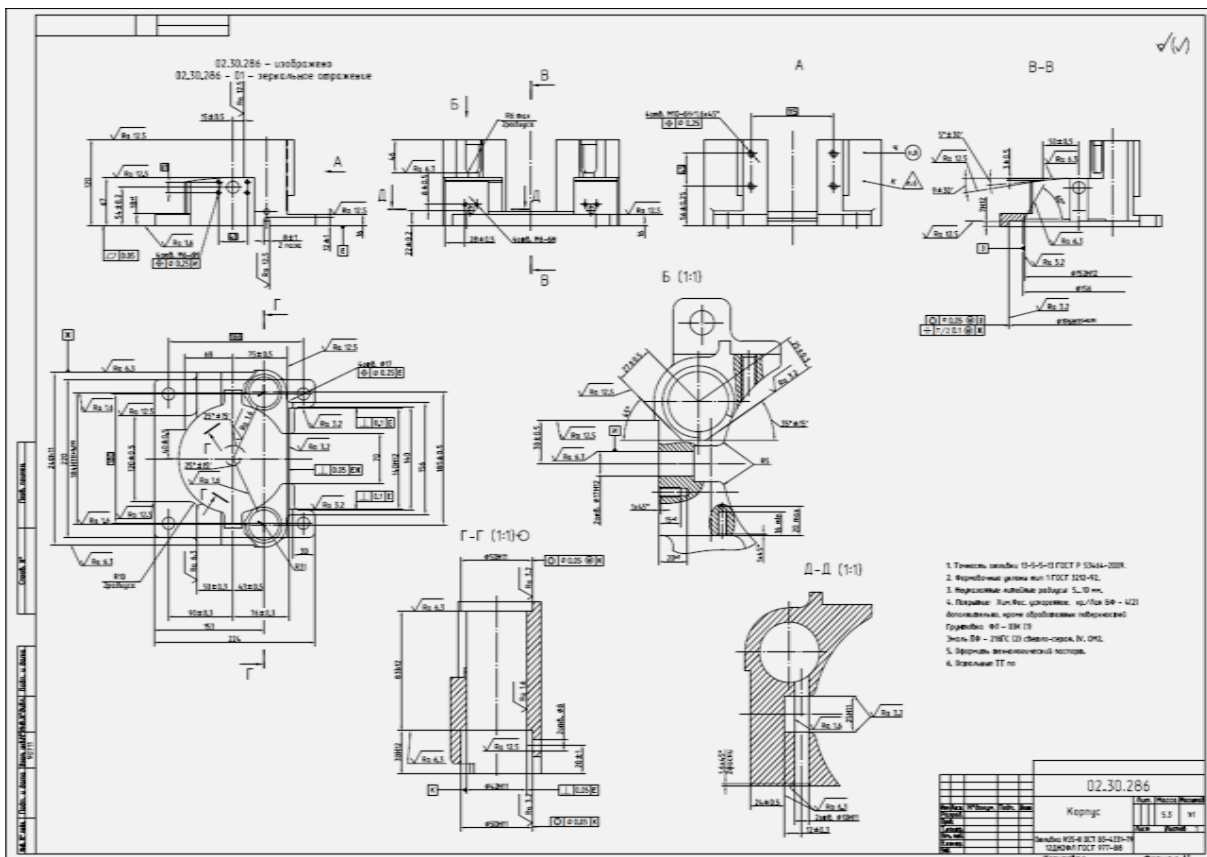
Технический многовидовый чертёж детали «Корпус»
